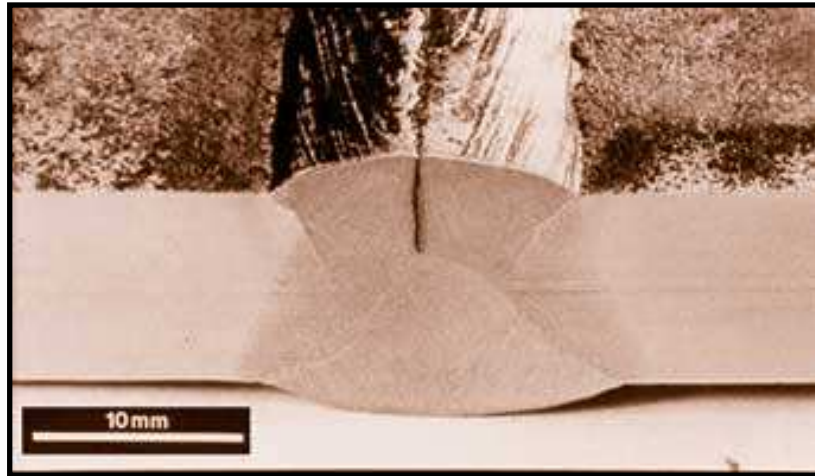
Fissure dans une Soudure en V double
